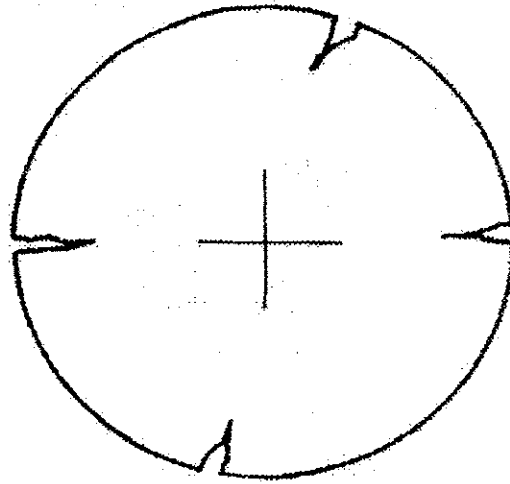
Trincas na zona de maior retração. Fonte: Facincani (1992).
